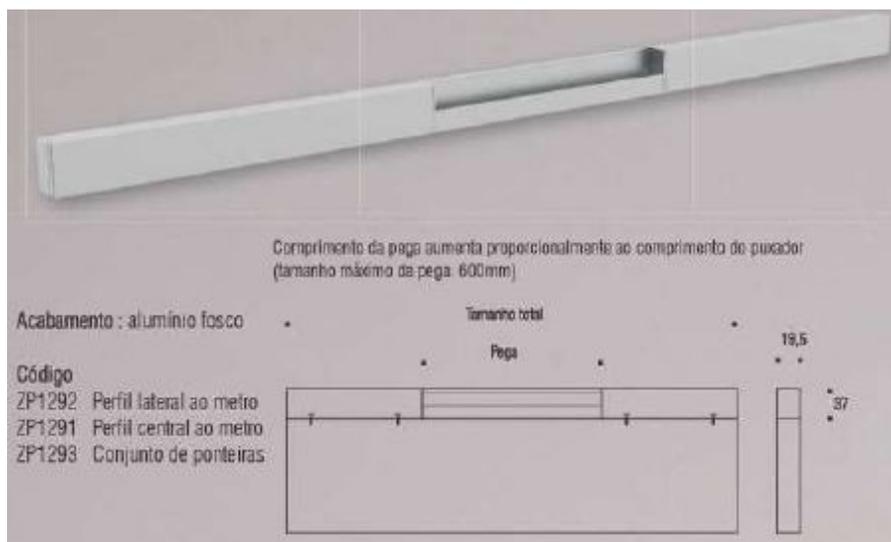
CROQUI DA MONTAGEM DO PUXADOR TIPO PERFIL LINEAR PRETENDIDO
